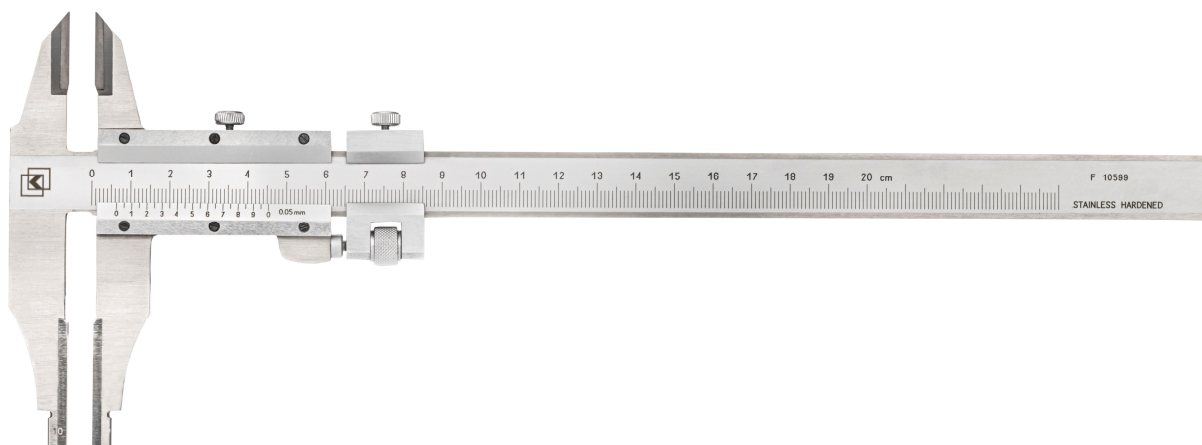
Общий вид штангенциркулей ШЦ-II с губками, оснащенными твердым сплавом
